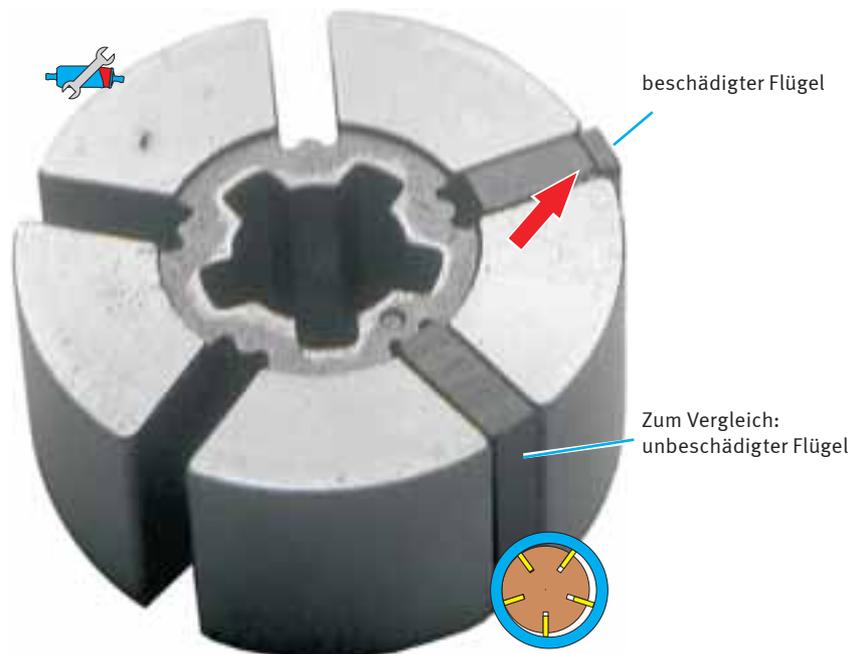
Pumpenwerk einer Flügelzellenpumpe - Schaden durch Fremdkörper
